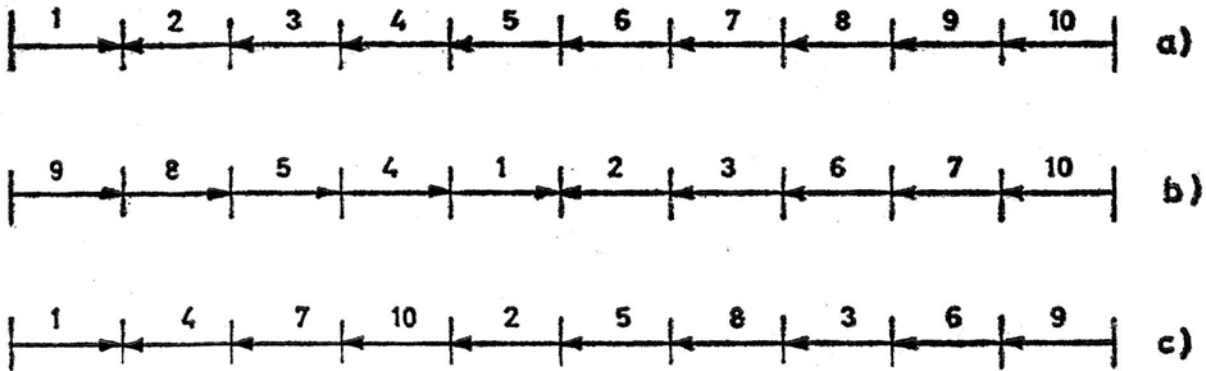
SOLDADURAS A PASO DE PEREGRINO CON UN SOLDADOR
